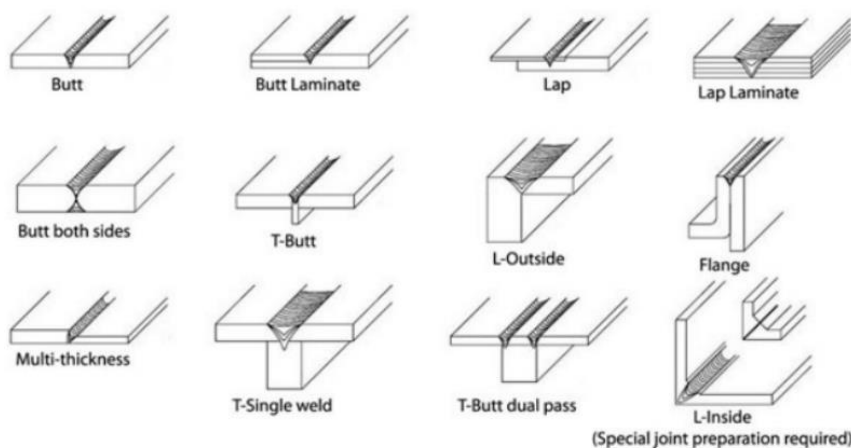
Configurations possibles pour le soudage par friction malaxage [Mishra 2016]
